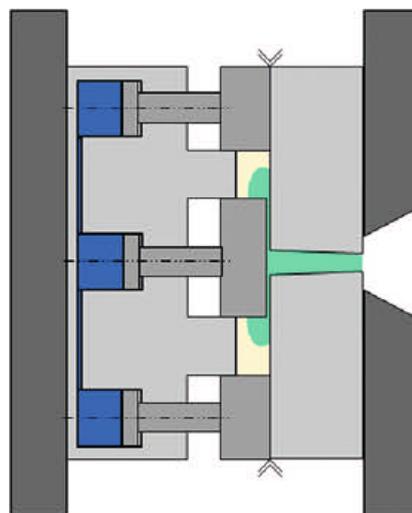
Prinzipskizze eines Prägewerkzeugs mit hydraulisch beaufschlagtem Kavitätenrahmen (blau = Hydrauliköl)
